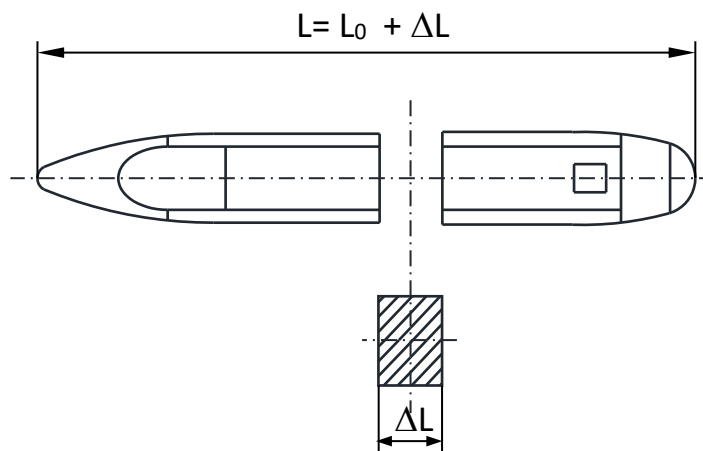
Збільшення корпусу судна за рахунок циліндричної вставки
